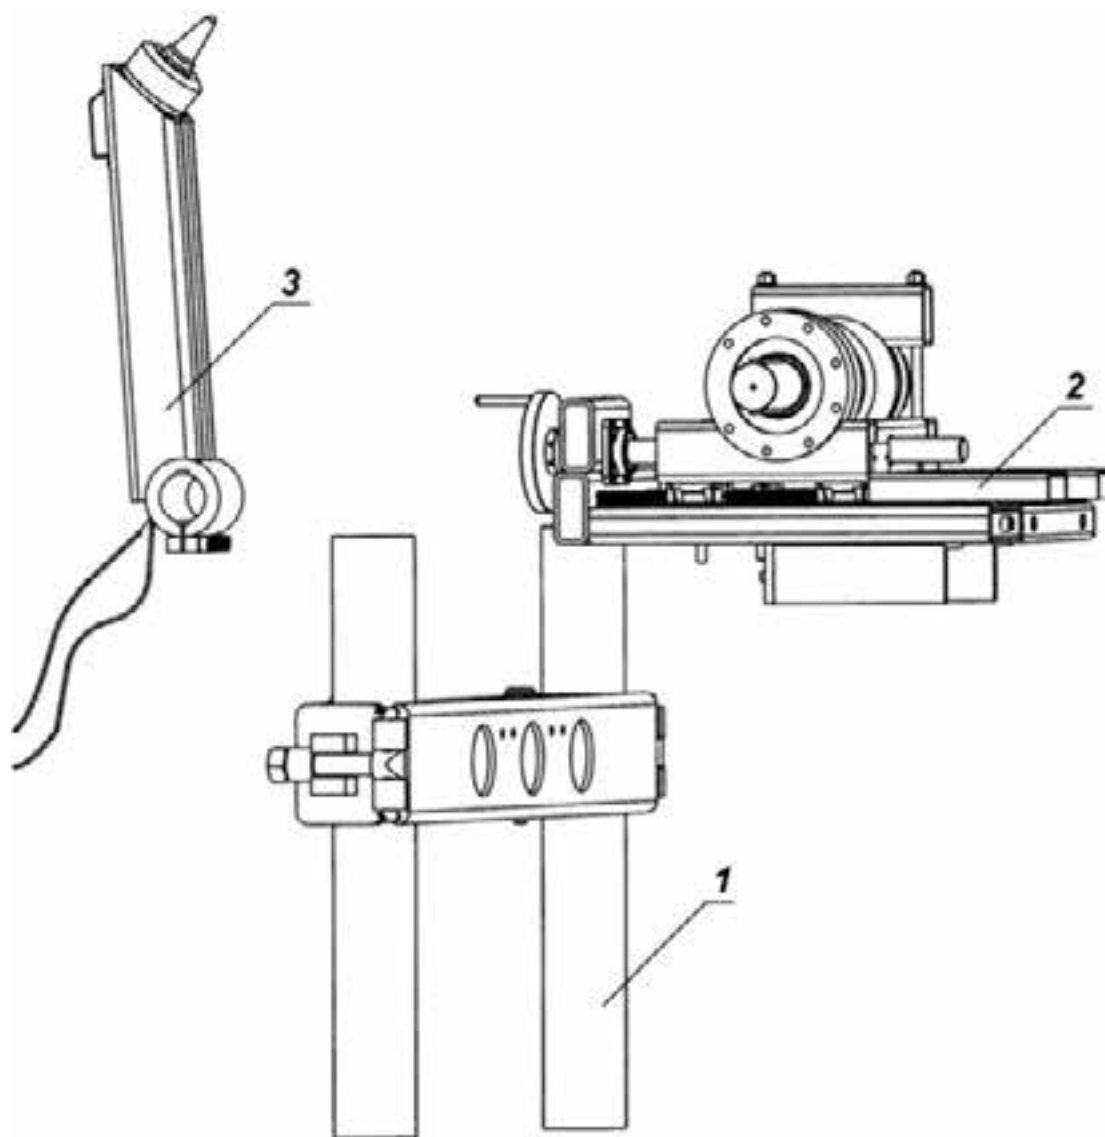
Widok przyrządu zmontowanego i gotowego do pracy
